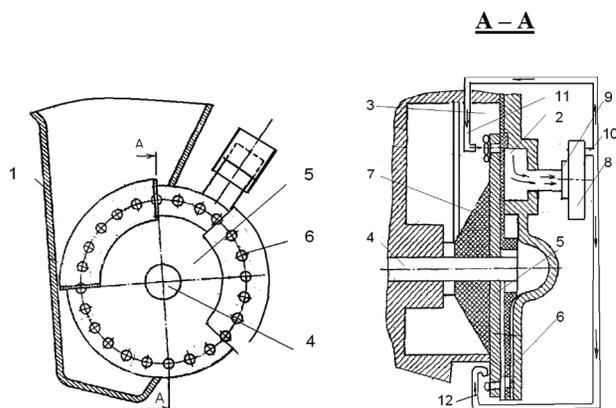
Макетный образец высевающего аппарата, работающего на вакууме: 1 – бункер для семян; 2 – камера разрежения; 3 – приемная семенная камера; 4 – ось; 5 – высевающий диск; 6 – отверстие; 7 – ворошилка семян; 8 – вентилятор; 9 – патрубок; 10 – нагнетающий патрубок; 11 и 12 – рукава.
